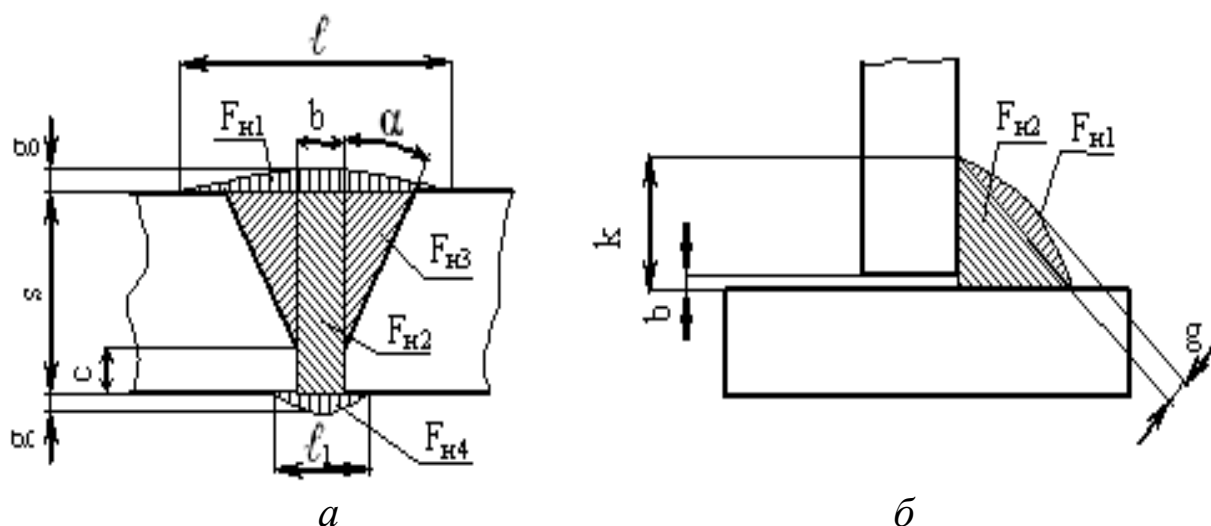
Схема разбивки сечения наплавленного металла:
